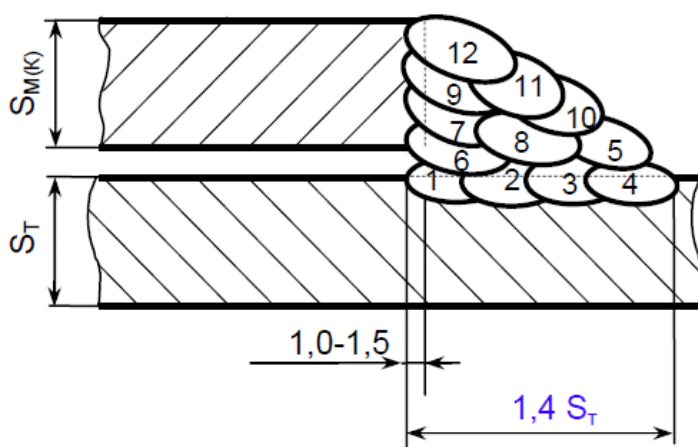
Последовательность сварки кольцевых угловых швов муфт
